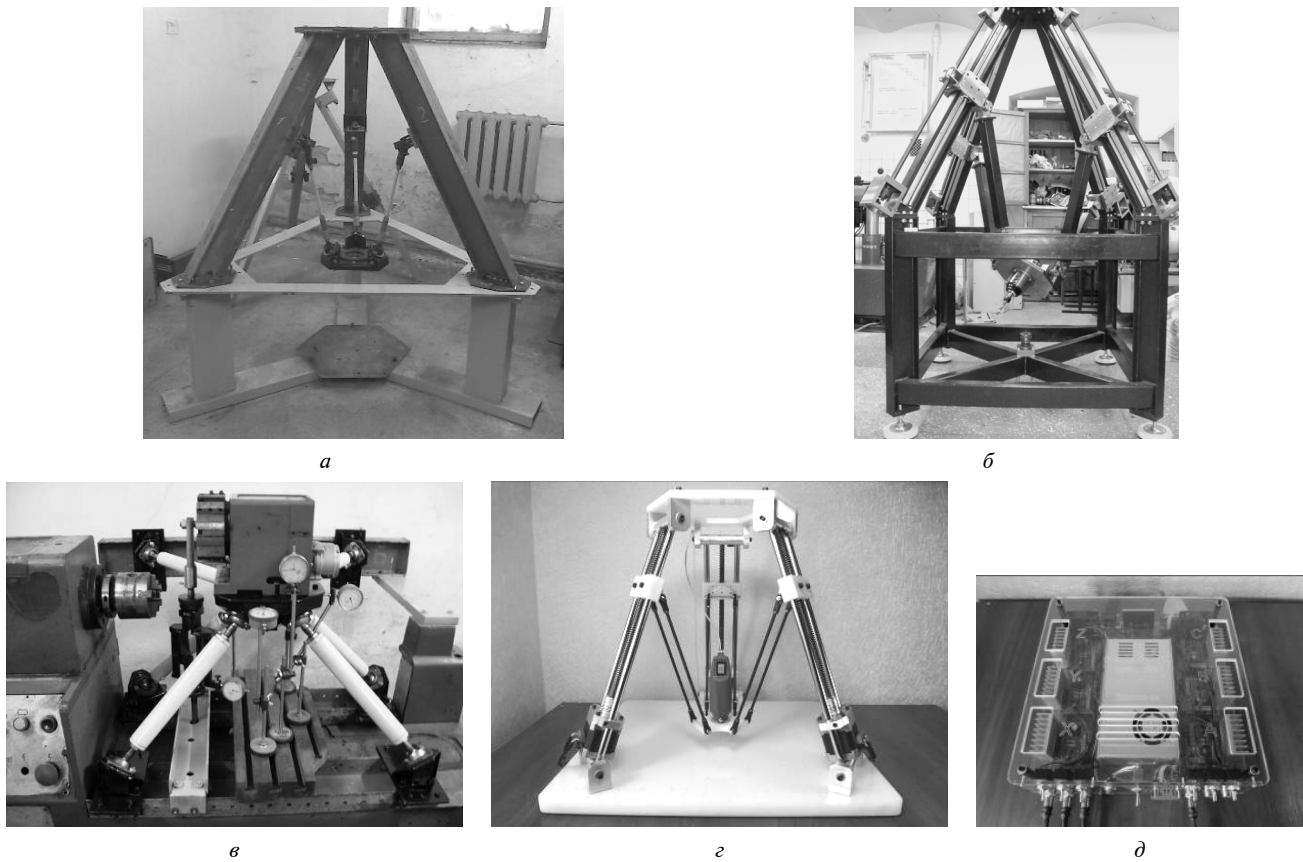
Виготовлені дослідні зразки верстатів з МПС каркасних компонок: *а* – каркасна компоновка трикоординатного свердильно-фрезерного верстата з МПС; *б* – каркасна компоновка п'ятикоординатного свердильно-фрезерного верстата з МПС; *в* – багатоцільовий токарний верстат-гексаглайд; *г* – діючий настільний верстат-триглайд пірамідальної каркасної компоновки; *д* – універсальний контролер системи керування верстатом-триглайдом
